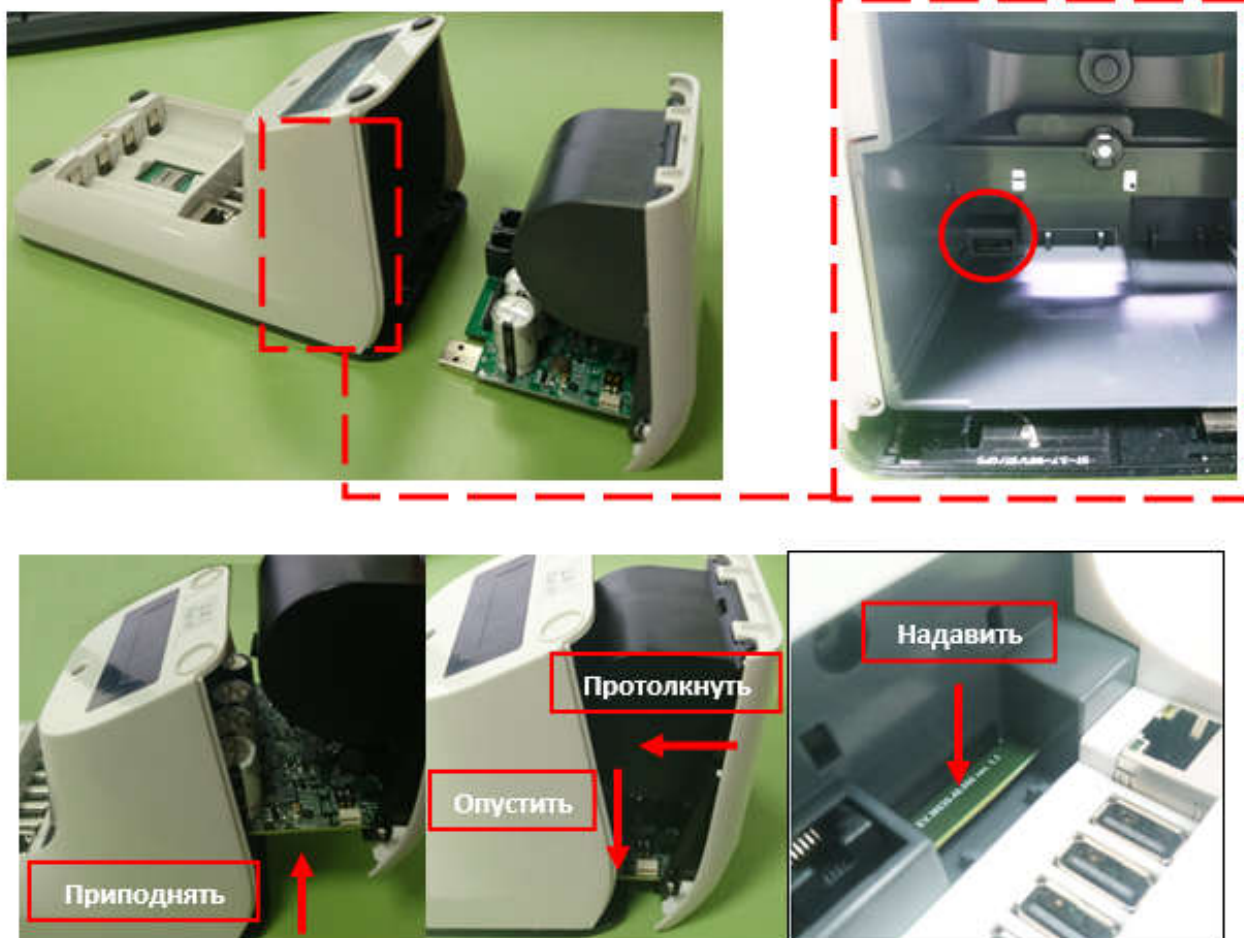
Установка лотка с модулем ФР в корпус СТ.
